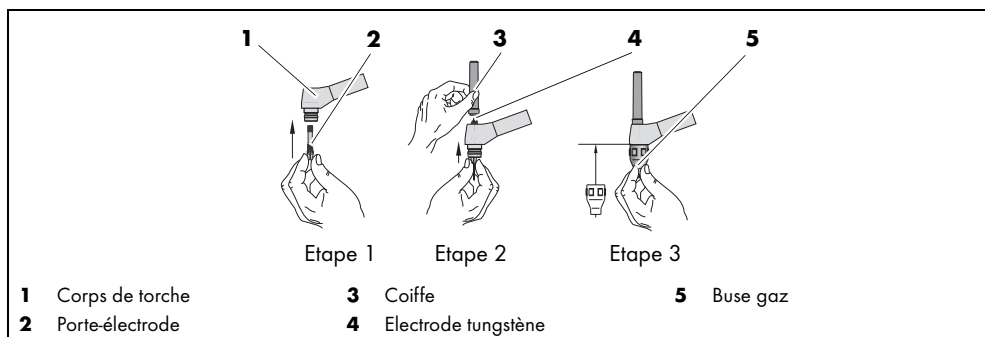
Torche de soudage ABITIG® Little 90, 180W
